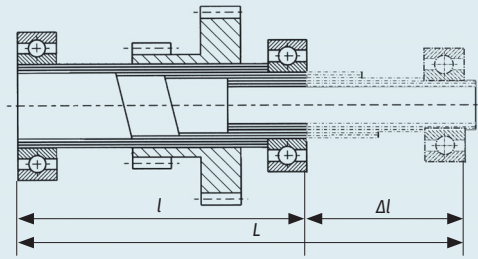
Навитый вал передачи в раздвинутом (штрих-пунктир) положении
